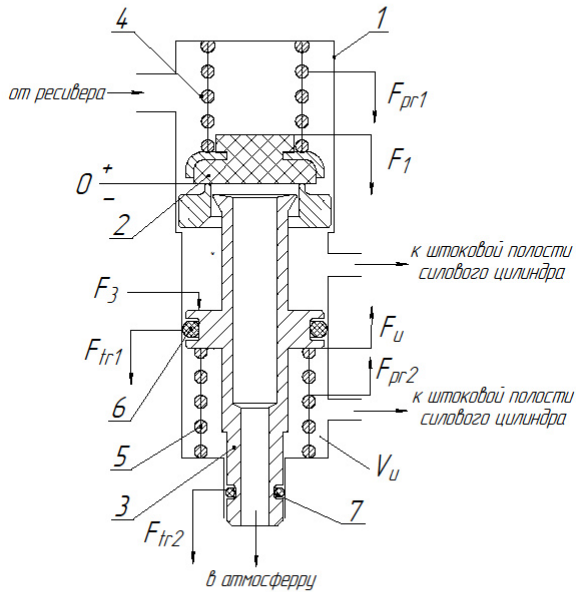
Расчётная схема ускорительного клапана: 1 – корпус; 2 – седло клапана; 3 – золотник; 4 – пружина клапана; 5 – пружина золотника; 6, 7 – уплотнительные кольца
